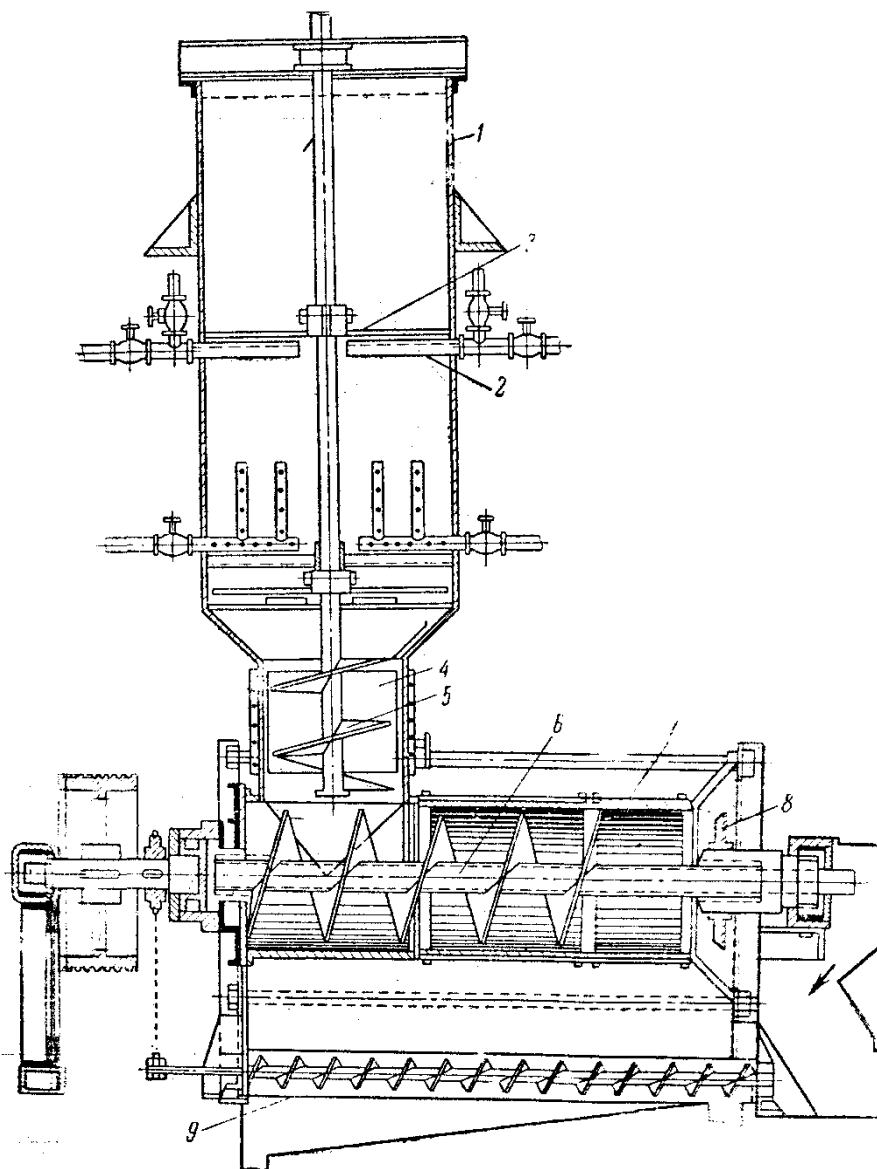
Схема форшнека КЯ: 1 – бункер; 2 – форсунки подачі пари; 3 – ножі-мішалки; 4 – патрубок; 5 – шнек-живильник; 6 – вал шнековий; 7 – циліндр-зеер; 8 – регулюючий конус; 9 – шнек для видалення олії.
